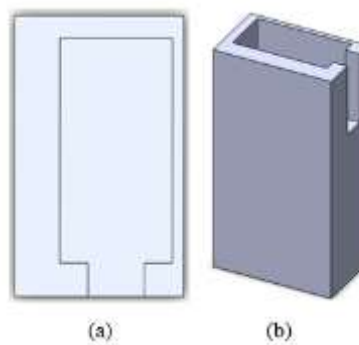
Soporte para motor. (a) Vista superior (b) Vista 3D
